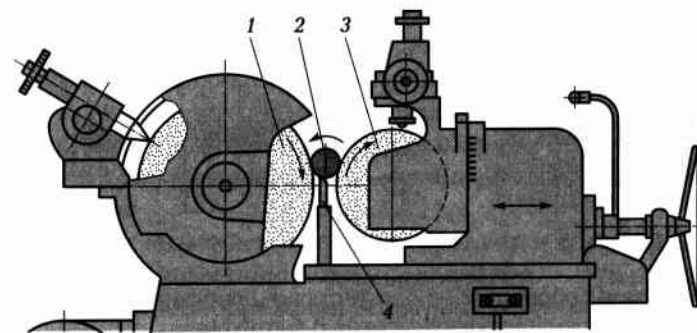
Общий вид бесцентрово-шлифовального станка
